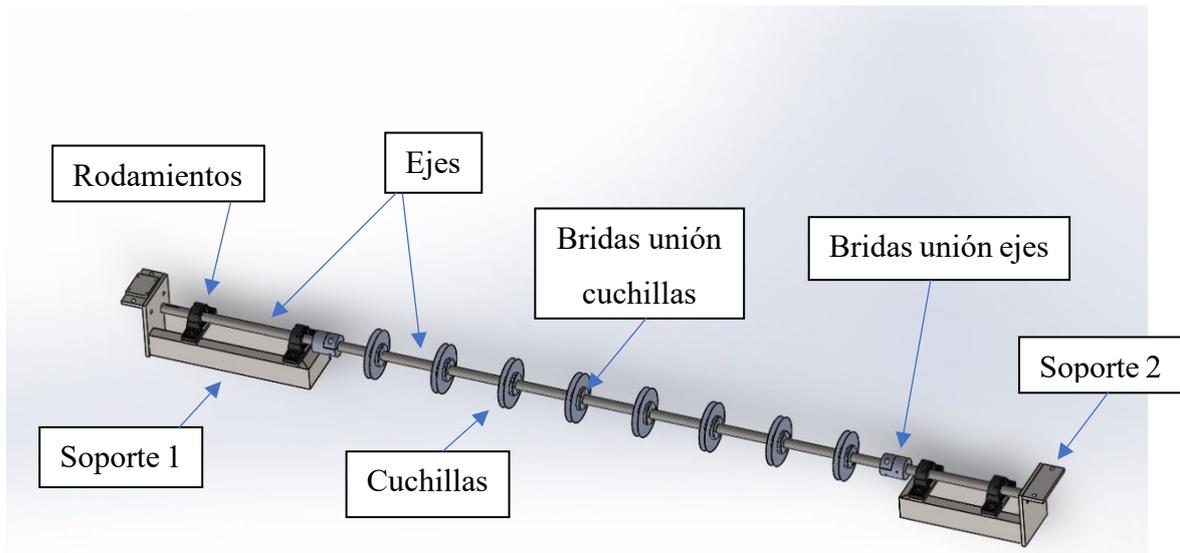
Imagen 3D de la máquina cortadora. Fuente: modelado SolidWorks
